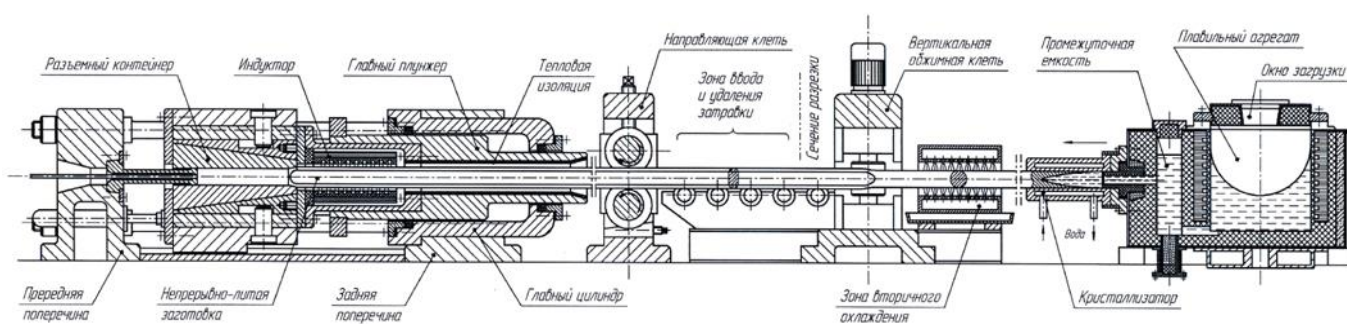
Схема литейно-прессового агрегата для производства прутков
